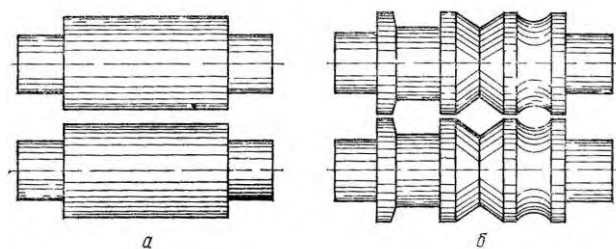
Валки с гладкой бочкой (а) и калиброванные валки (б)
